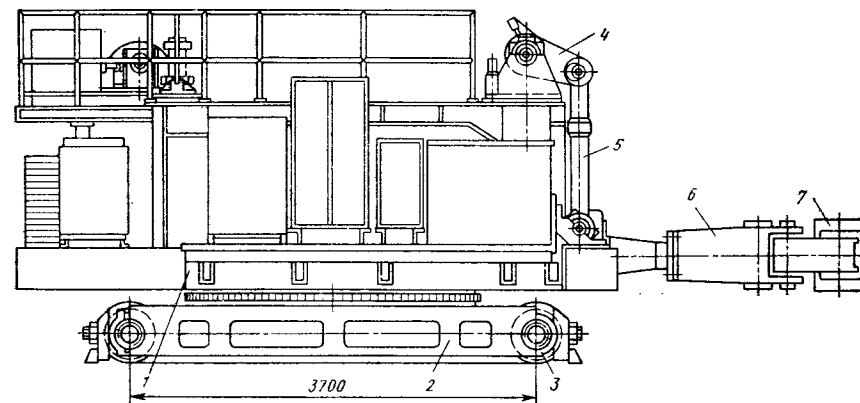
Манипулятор ковочный грузоподъемностью 50 кН: 1 — поворотная рама; 2 — тележка; 3 — ходовые колеса; 4 — механизм подъема и выравнивания хобота; 5 — гидроцилиндры механизма подъема; 6 — хобот; 7 — клещи
